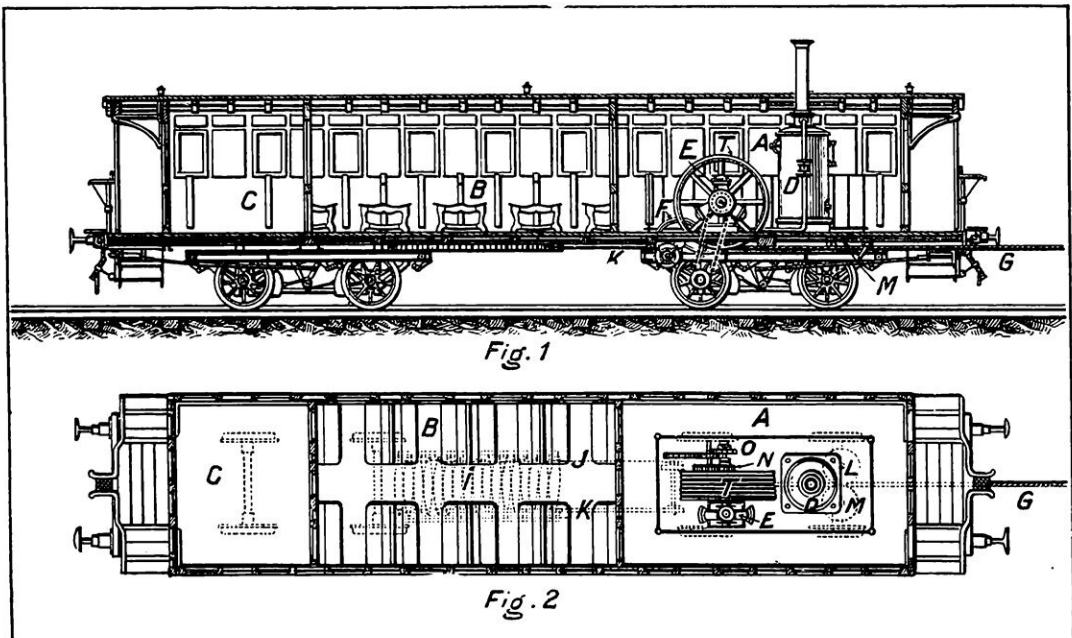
VOITURE ATTENDANT LE PASSAGE D'UN EXPRESS POUR ÊTRE ACCROCHÉE PAR LUI (VUE EN ÉLEVATION ET EN COUPE). — FIG. 2. LA MÊME VOITURE, VUE EN PLAN ET EN COUPE
